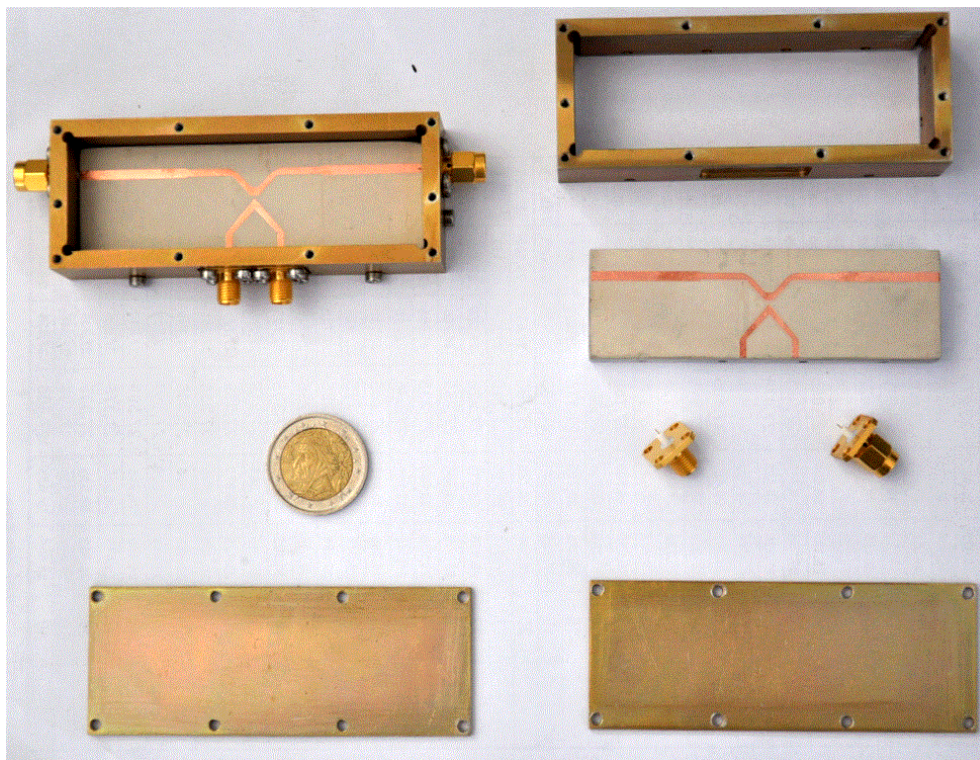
Fotografia del componente assemblato e di fianco quello completamente smontato
